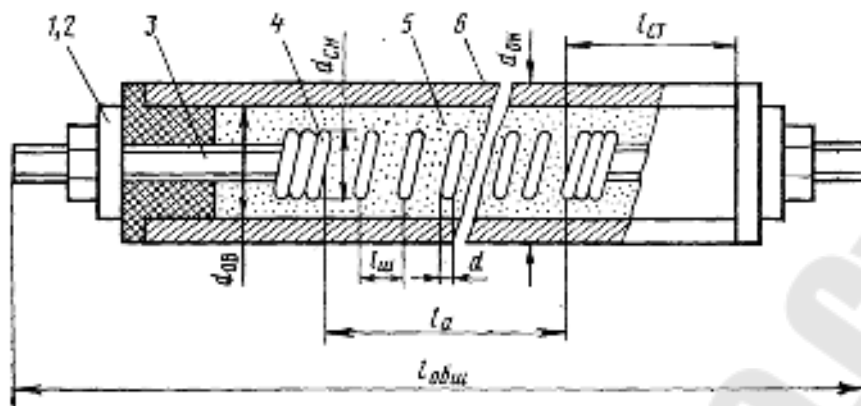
Трубчатый электронагреватель (ТЭН): 1 и 2 – контактное устройство; 3 – контактный стержень; 4 – нагревательная спираль; 5 – наполнитель (периклаз); 6 – оболочка (трубка) ТЭН; $l_{ст}$ – длина контактного стержня в заделке; $l_{общ}$ – общая длина
